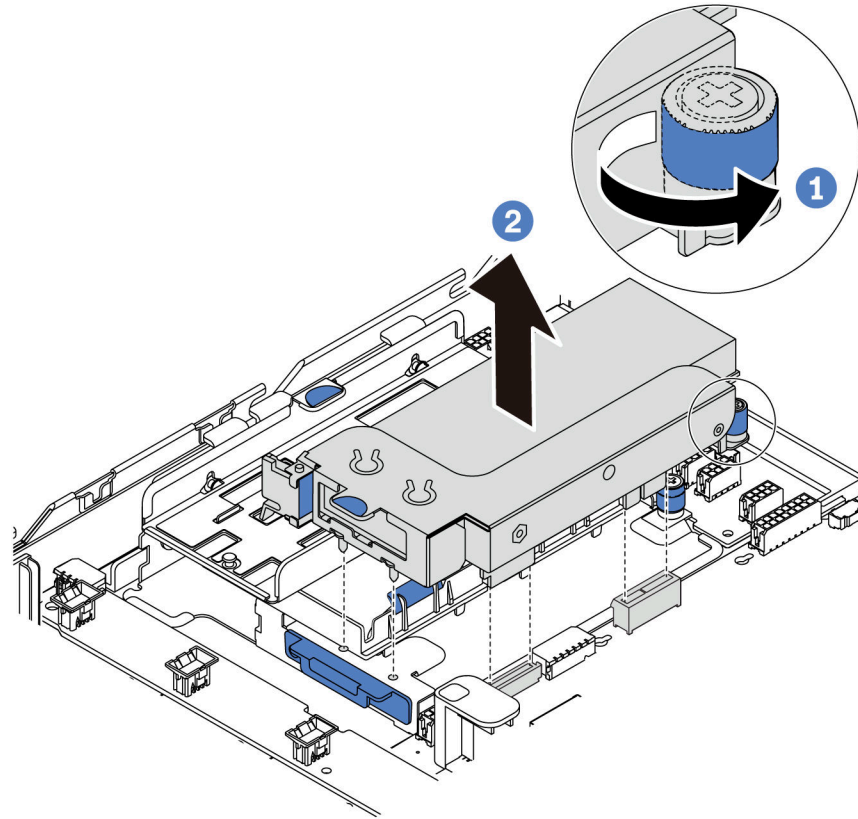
Entfernen der internen Adapterkartenbaugruppe
